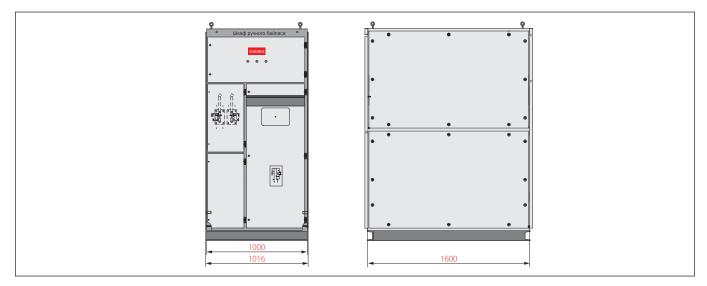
Корпус шкафа ручного байпаса типоразмера МВ04
